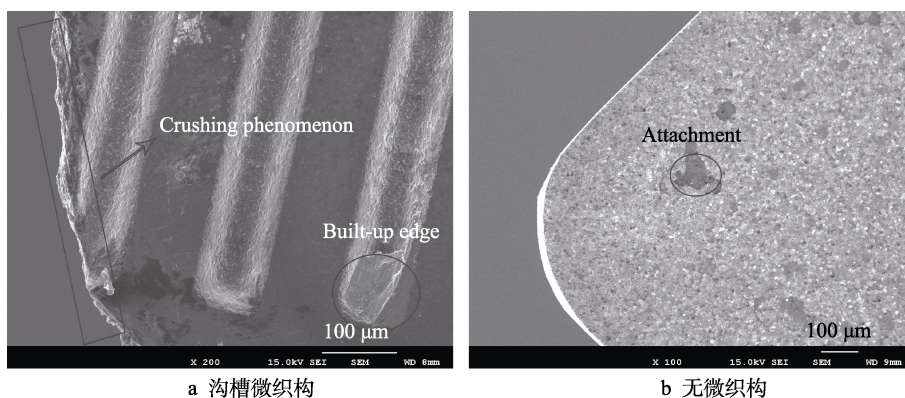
PCD 刀具前刀面在干切削下的磨损形貌
